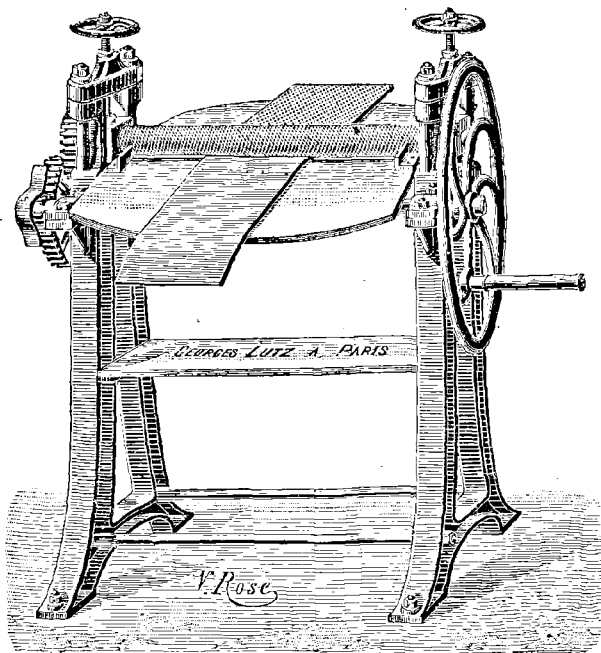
Machine à chagriner ou à quadriller par changement de cylindre (G. Lutz, Krempp, successeur).
